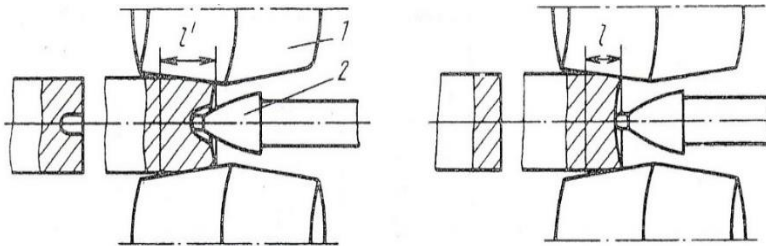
Схеми осередків деформації в прошивному стані при прониканні оправки в торець зацентрованої (а) і нецентрованої (б) заготовки [1]: 1 – валок; 2 – оправка
